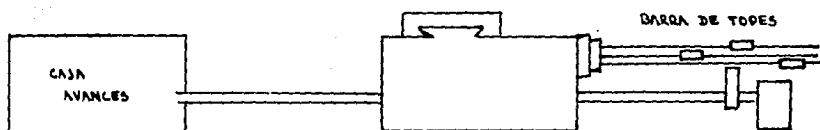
Posicionamiento de los toques mecánicos en una máquina herramienta.
